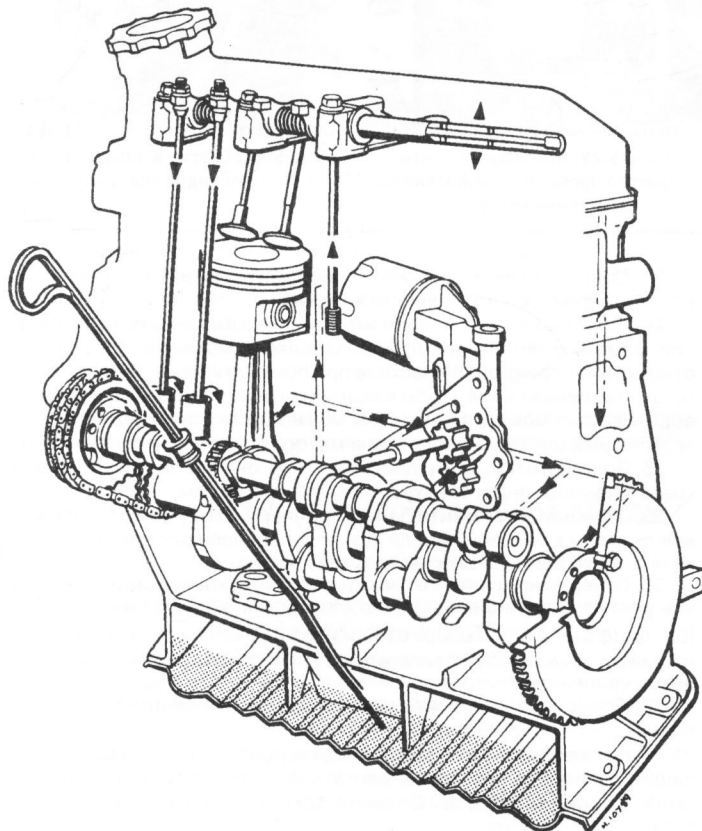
Детали системы смазки двигателя (Раздел 1)
